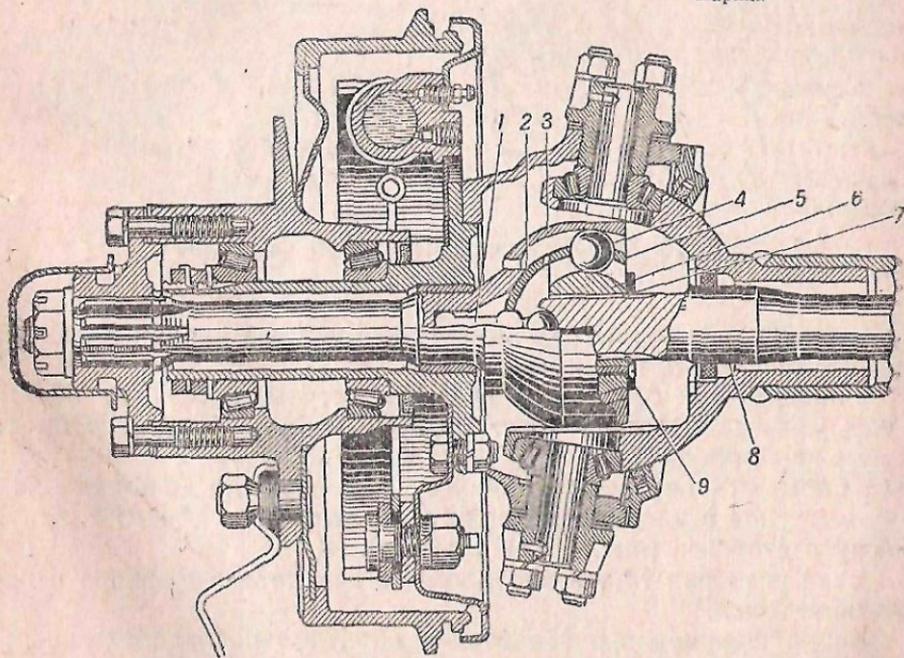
Поворотная цапфа и привод переднего колеса с шарниром „Рцепп“:
